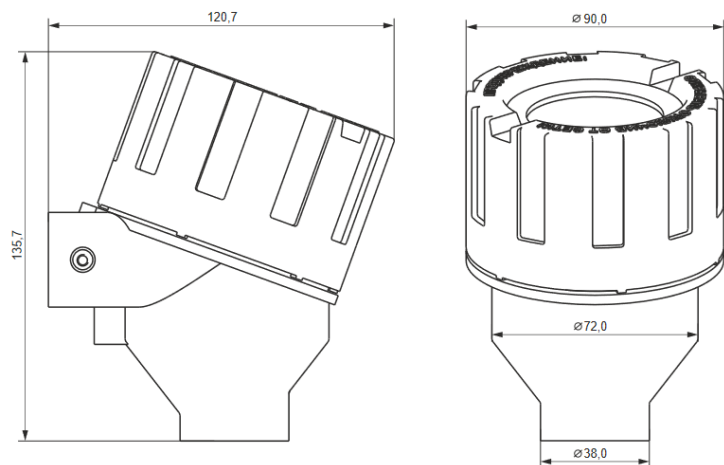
Габаритные размеры ИП 0304/МЗ-Н-ХДАД-И,
